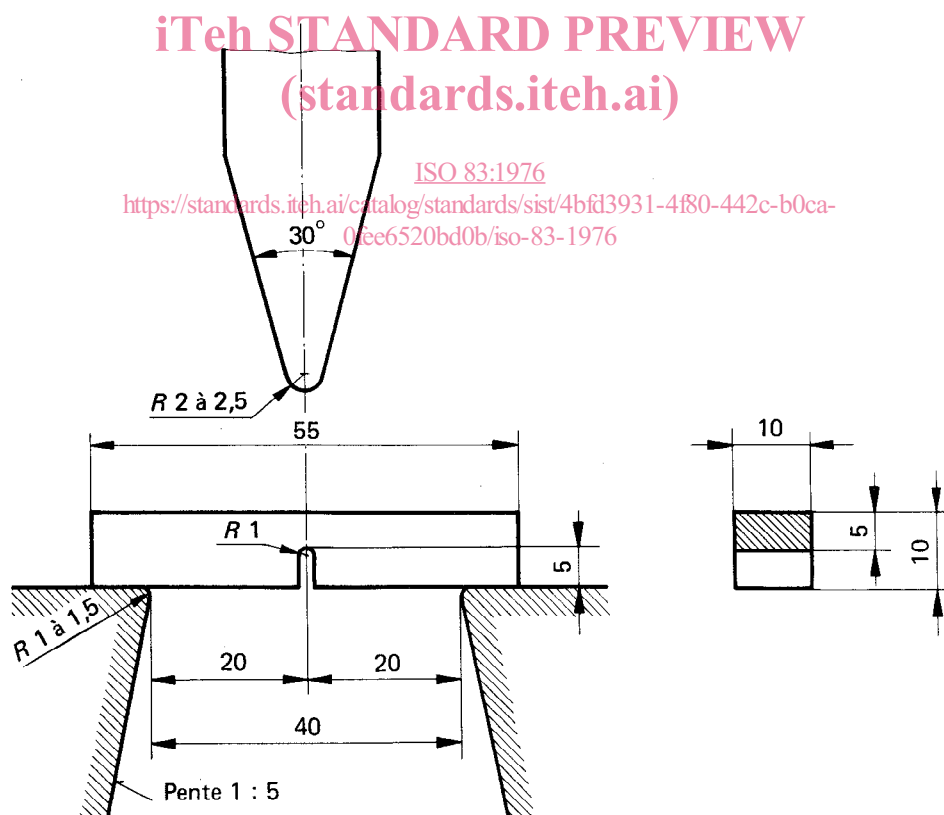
Essai de résilience Charpy (entaille en U) – Dimensions
